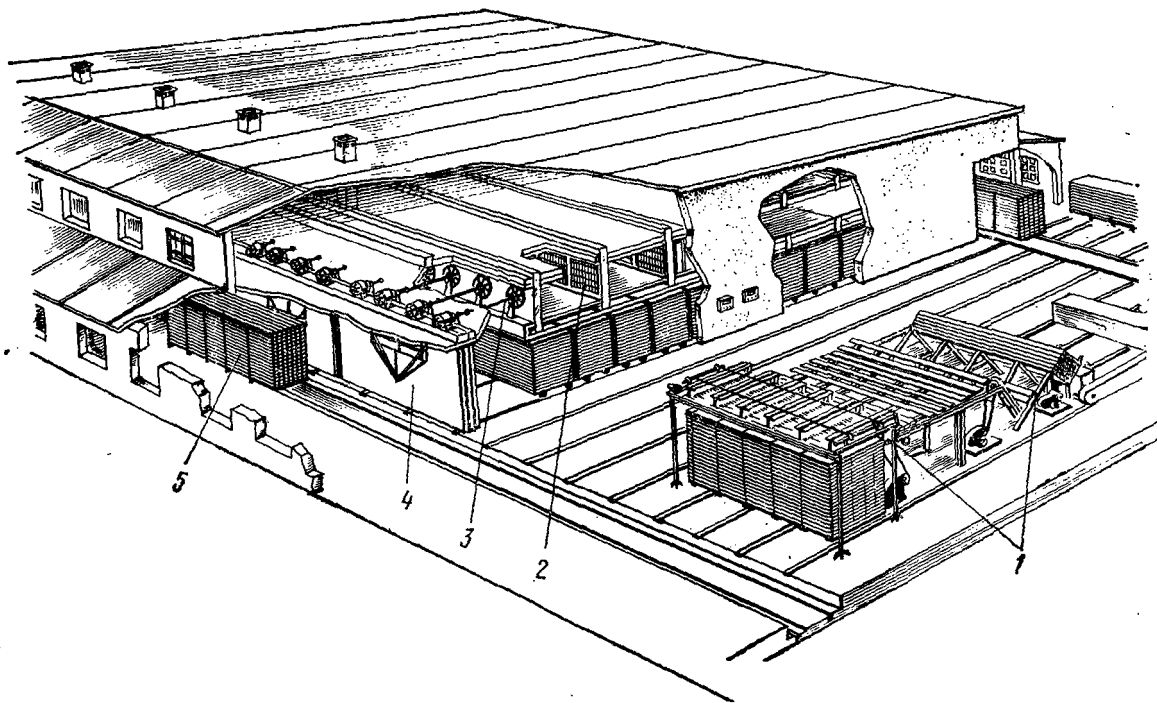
Сушильные камеры непрерывного действия ЦНИИМОД-49 с противоточной прямой циркуляцией и поперечной загрузкой штабелей:
